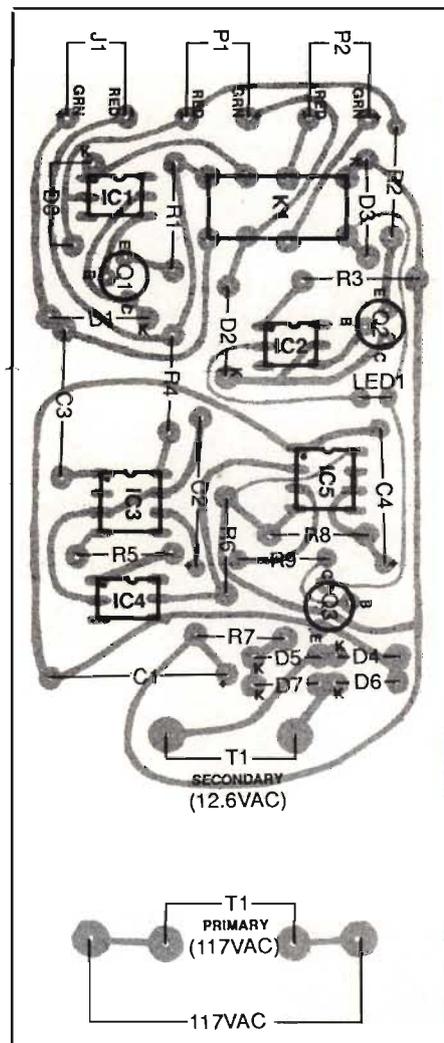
Guida dei collegamenti sulla piastra (da seguire anche con l'utilizzo di piastre preforate).
